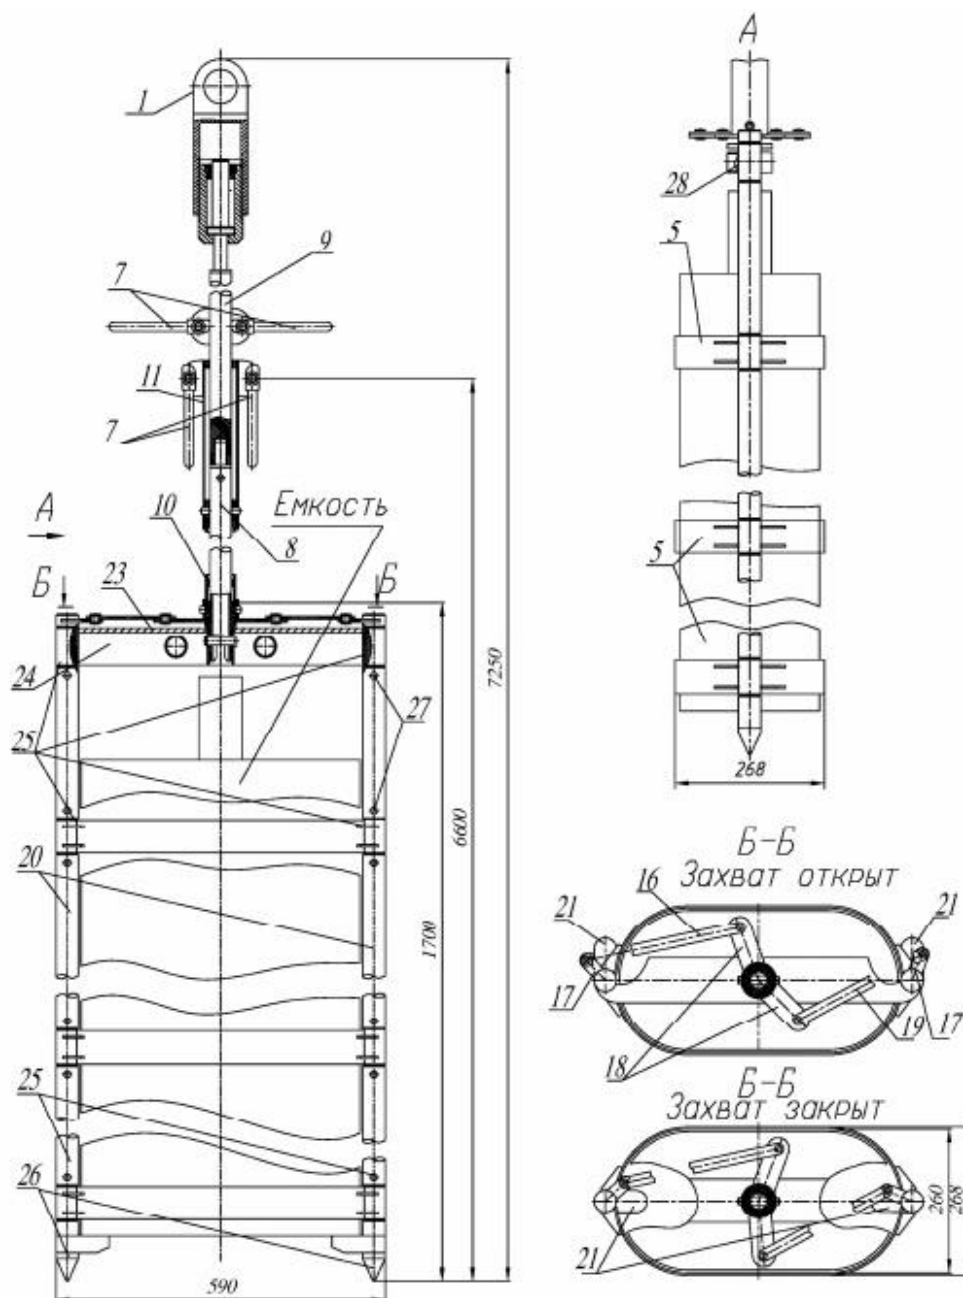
,а. Разрез приспособления для захвата и подъема емкости: 1 – петля; 2 – гайка; 3 – втулка; 4 – упор; 5 – хомут; 6 – шпилька; 7 – ручка; 8 – тяга; 9 – вставка; 10 – труба; 11 – втулка; 12 – направляющая; 13 – втулка; 14 – втулка; 15 – ось; 16 – рычаг; 17 – рычаг; 18 – рычаг; 19 – рычаг; 20 – стойка; 21 – захват; 22 – штифт; 23 – пластина; 24 – ребро; 25 – втулка; 26 – наконечник; 27 – штифт; 28 – втулка
